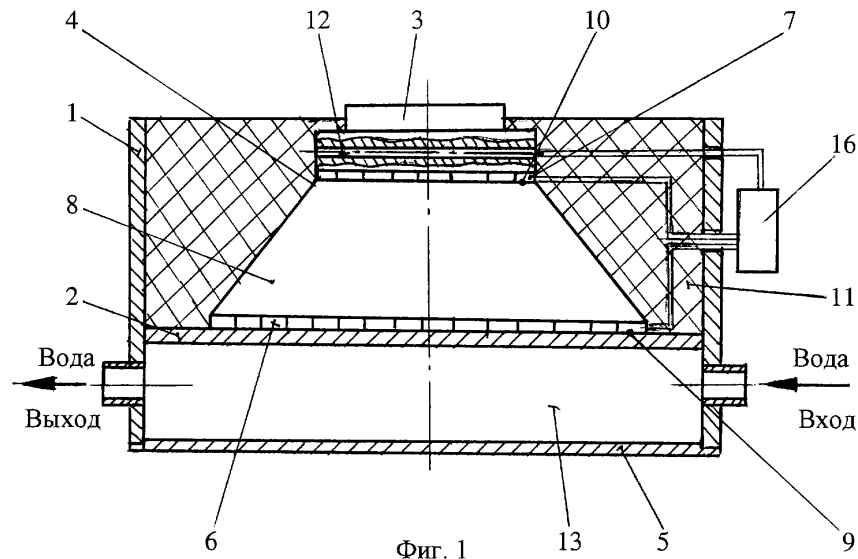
Термоелектричний пристрій для контактного охолодження поверхонь
